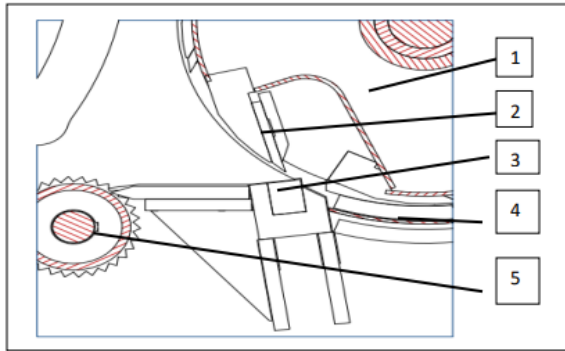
Схема ділянки подрібнювання та подавання матеріалів барабанної деревинорубальної машини: 1 – ножовий барабан; 2 – різальний ніж; 3 – контрніж; 4 – калібрувальне сито; 5 – нижній зубчастий валець механізму подавання
